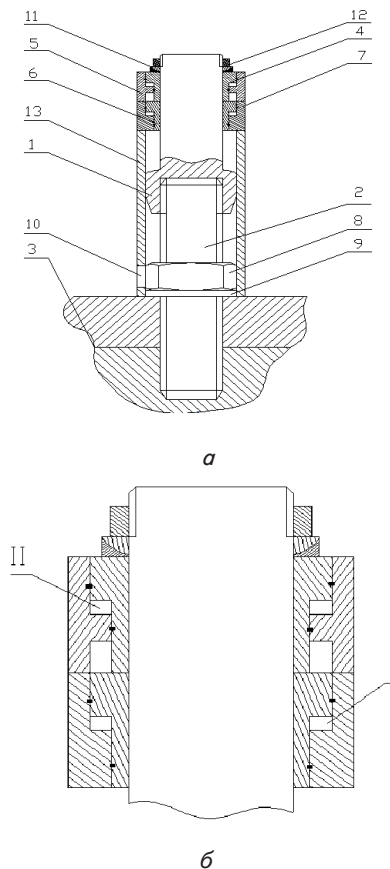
Схема процесу ущільнення та принципу дії гідроциліндру: 1 – шток; 2 – шпилька; 3 – площина ущільнення; 4 – верхній поршень; 5 – верхній циліндр; 6 – нижній поршень; 7 – нижній циліндр; 8 – гайка; 9 – шайба; 10 – вікно доступу до гайки; 11 – сферична шайба; 12 – стопор; 13- опорна втулка; I – порожнина нижнього циліндру, II – порожнина верхнього циліндру; а – схема взаємного розташування виконуючого механізму та площини ущільнення, б – каскадне розташування силових гідроциліндрів виконуючого механізму
